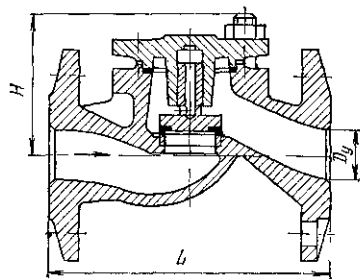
Клапан обратный подъемный фланцевый 16кч9п1 и 16кч9пж
